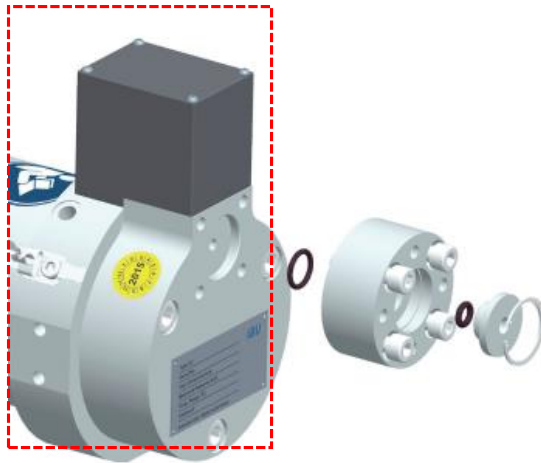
Vista detallada para ensamblaje del sujetador del inyector.
